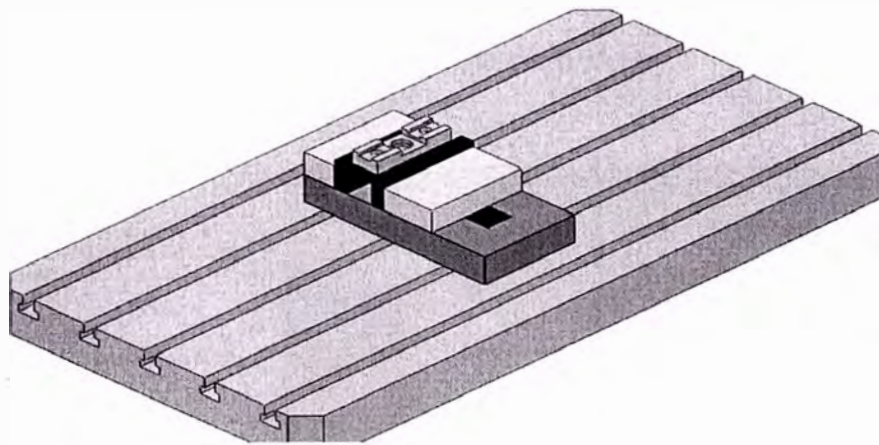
/ MONTAJE DE PIEZA EN FRESADORA / FUENTE:
